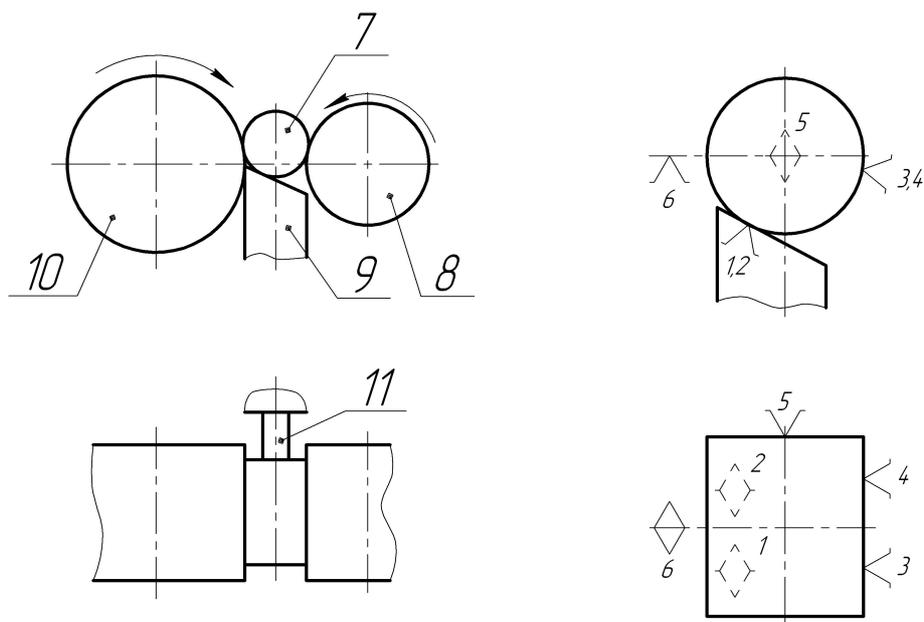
Установка заготовки по обрабатываемой поверхности при бесцентровом врезном шлифовании: 1 – 6 – опорные точки; 7 – заготовка; 8 – ведущий круг; 9 – опоры; 10 – шлифующий круг; 11 – продольный
